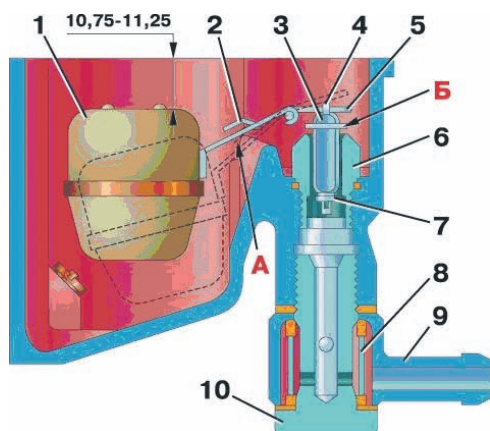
Поплавок і паливний клапан: 1 – поплавок; 2 – язичок; 3 – паливний клапан; 4 – сережка; 5 – язичок; 6 – сідло паливного клапана; 7 – шайба ущільнювача (е ластичний замочний елемент); 8 – паливний фільтр; 9 – штуцер паливопровода; 10 – паливопровідний болт
